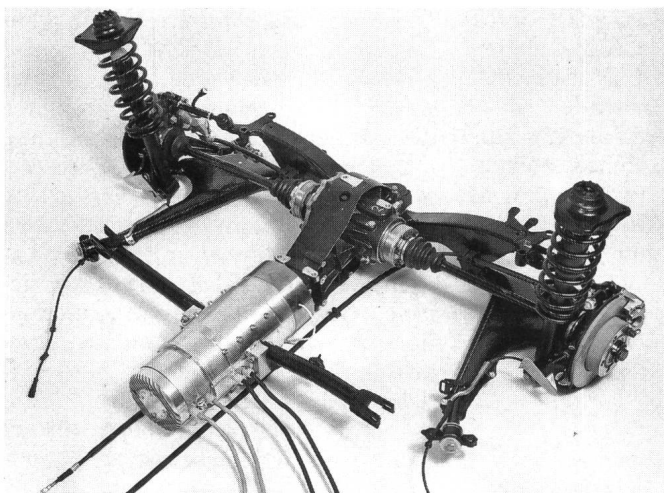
Der 9,3-kW-Gleichstrom-Reihenschlussmotor für den Hinterachsantrieb findet im Tunnel für die Kardanwelle Platz
